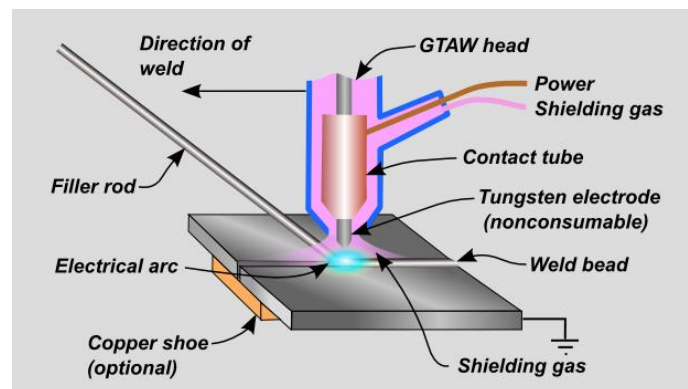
Elementos Principales de la Soldadura TIG
